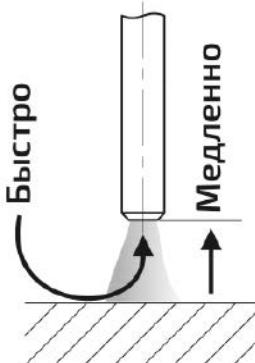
Способы зажигания сварочной дуги.
